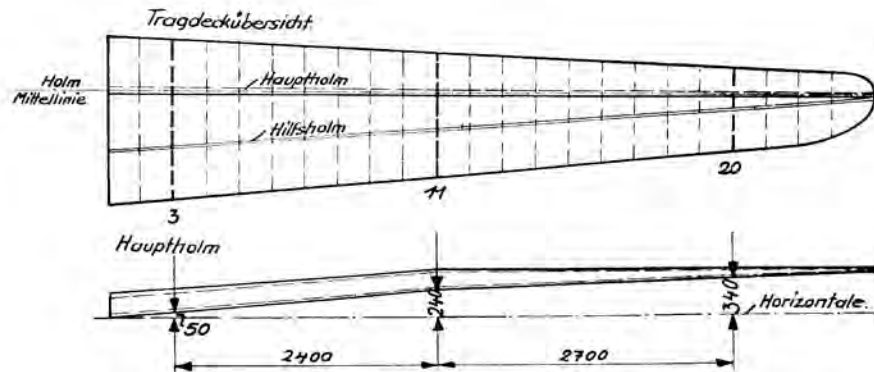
Tragdeckübersicht mit Holmzeichnung. Der Holm ist bei Rippe 11 geknickt.
